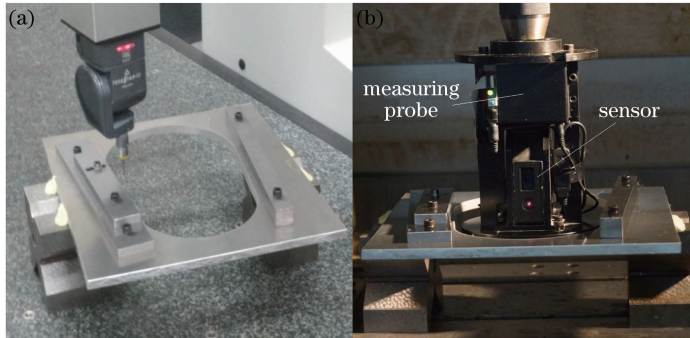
测量过程图。(a) CMM 打点测量; (b) CNC 在机测量
